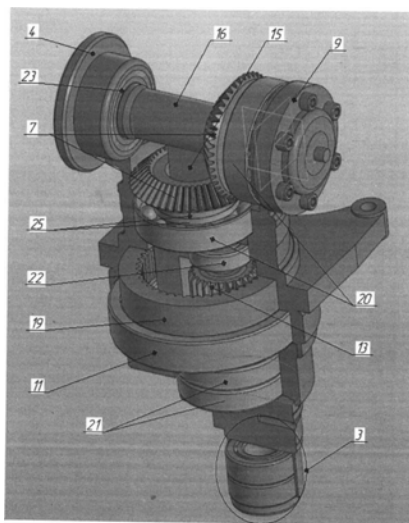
3D-модель зубчато-эксцентриккового механизма
